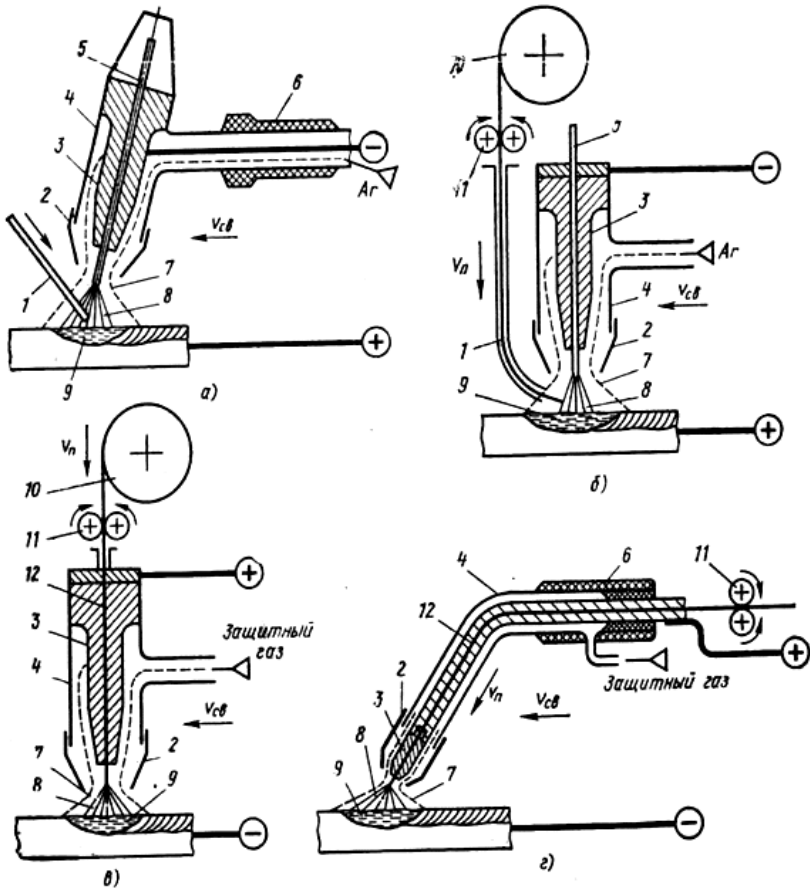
Виды дуговой наплавки в защитных газах:
